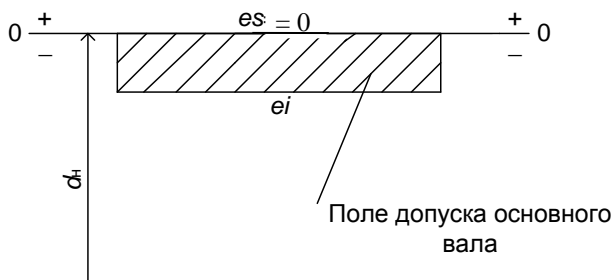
Пример изображения поля допуска основного вала
